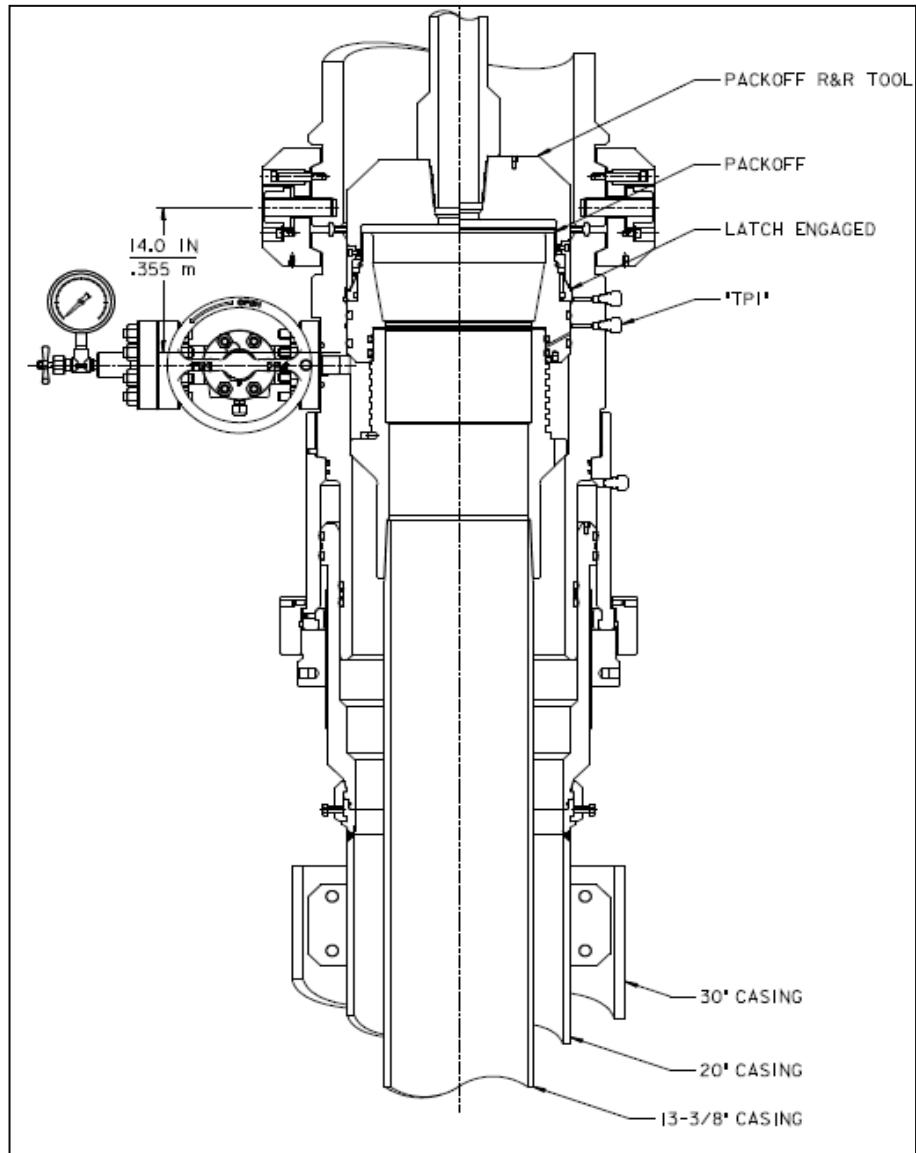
Installation de 13 3/8" CM Latch Packoff.
